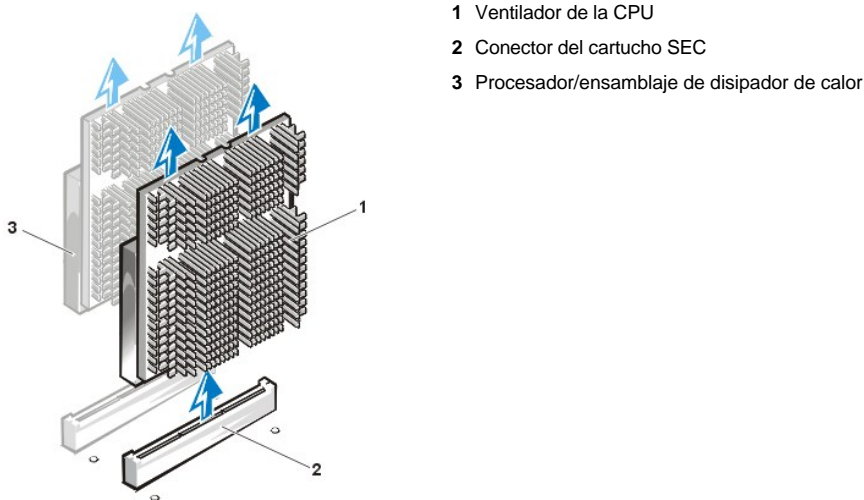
Desmontaje del cartucho SEC/ensamblaje de disipador de calor
